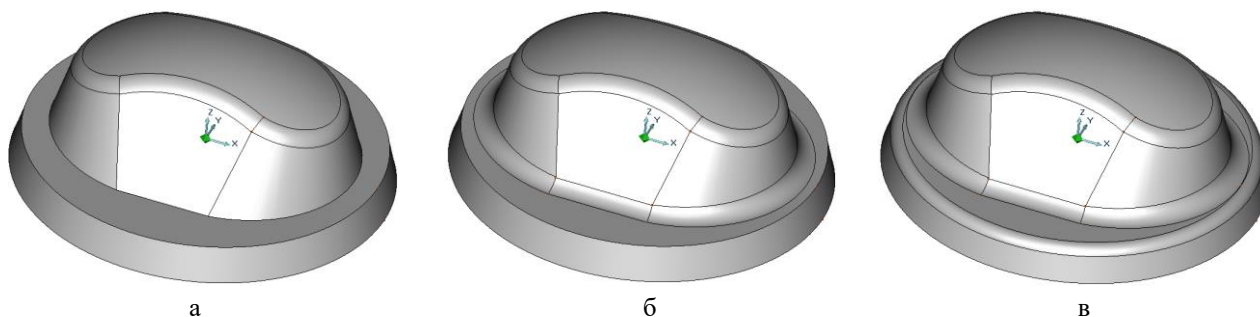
Скругление рёбер на внешней поверхности детали
